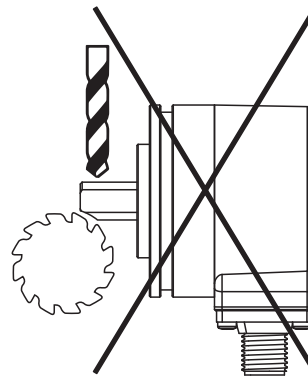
Montageansicht – nicht nachträglich bearbeiten
